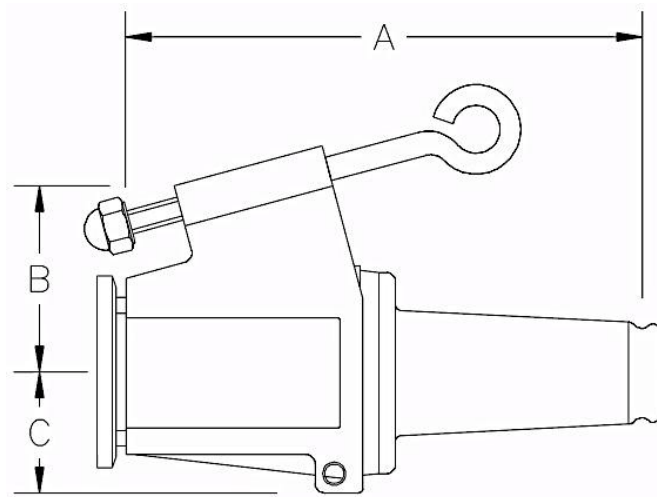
Dimensiones de boquilla tipo inserto estacionaria, [12].
